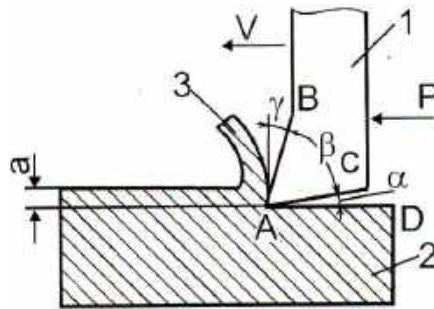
Схема процесу різання: 1 – інструмент (різальний клин); 2 – деталь, що обробляється; 3 – стружка; а – припуск
